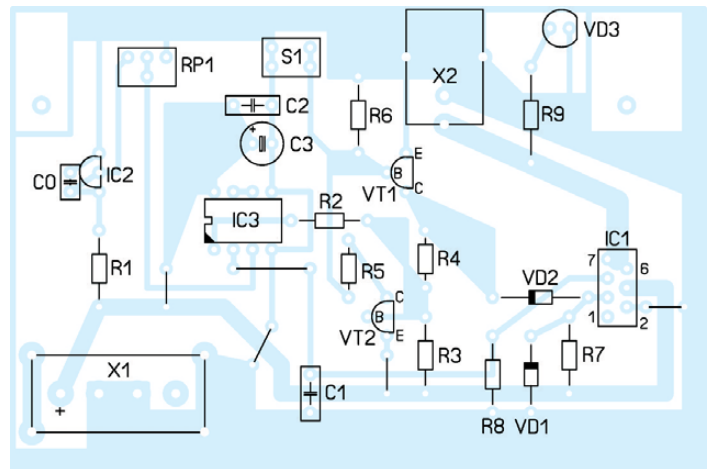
Bestückung der Leiterplatte für die Schutzschaltung 3; IC1 ist wiederum stehend einzulöten.
